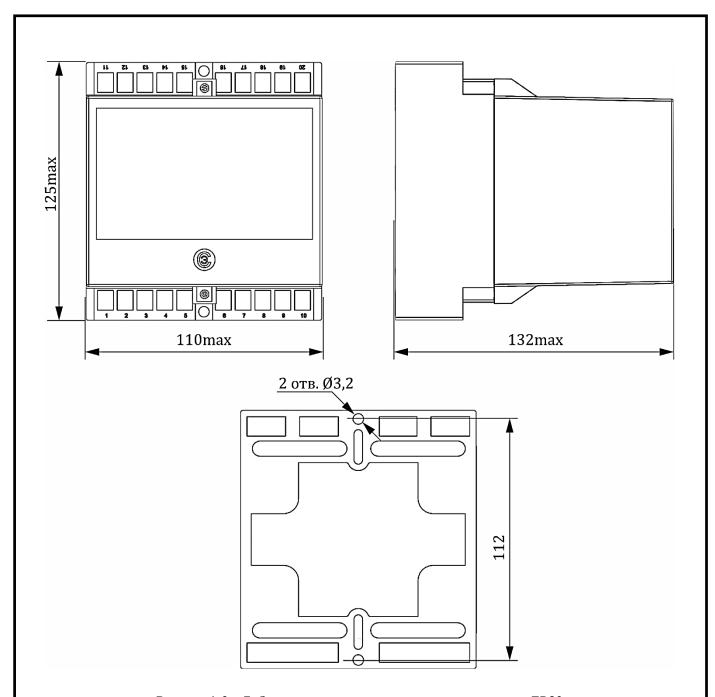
Габаритные и установочные размеры корпуса ЕВ20
